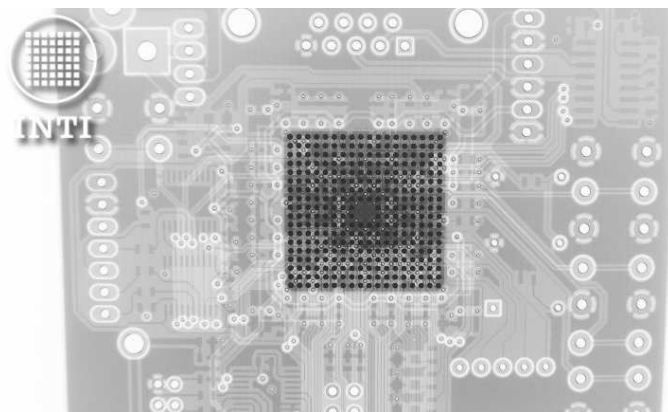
Radiografía de la placa S3Proto-mini con el chip BGA soldado.
